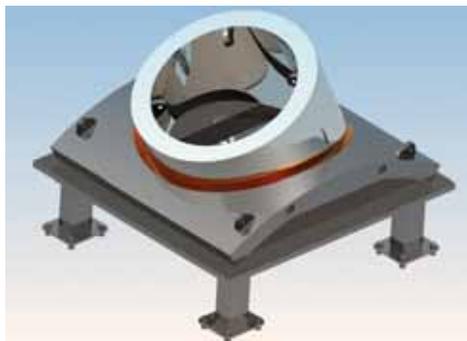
Натурный макет для отработки технологии автоматической сварки
